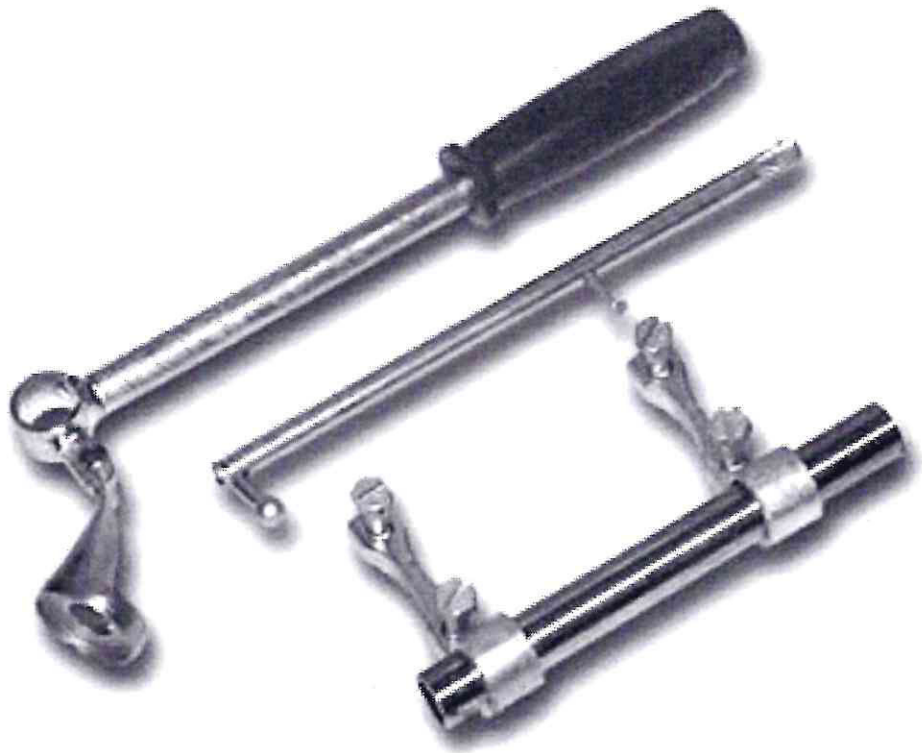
Приспособление для снятия клапанных пружин двигателя ВАЗ-2112.
